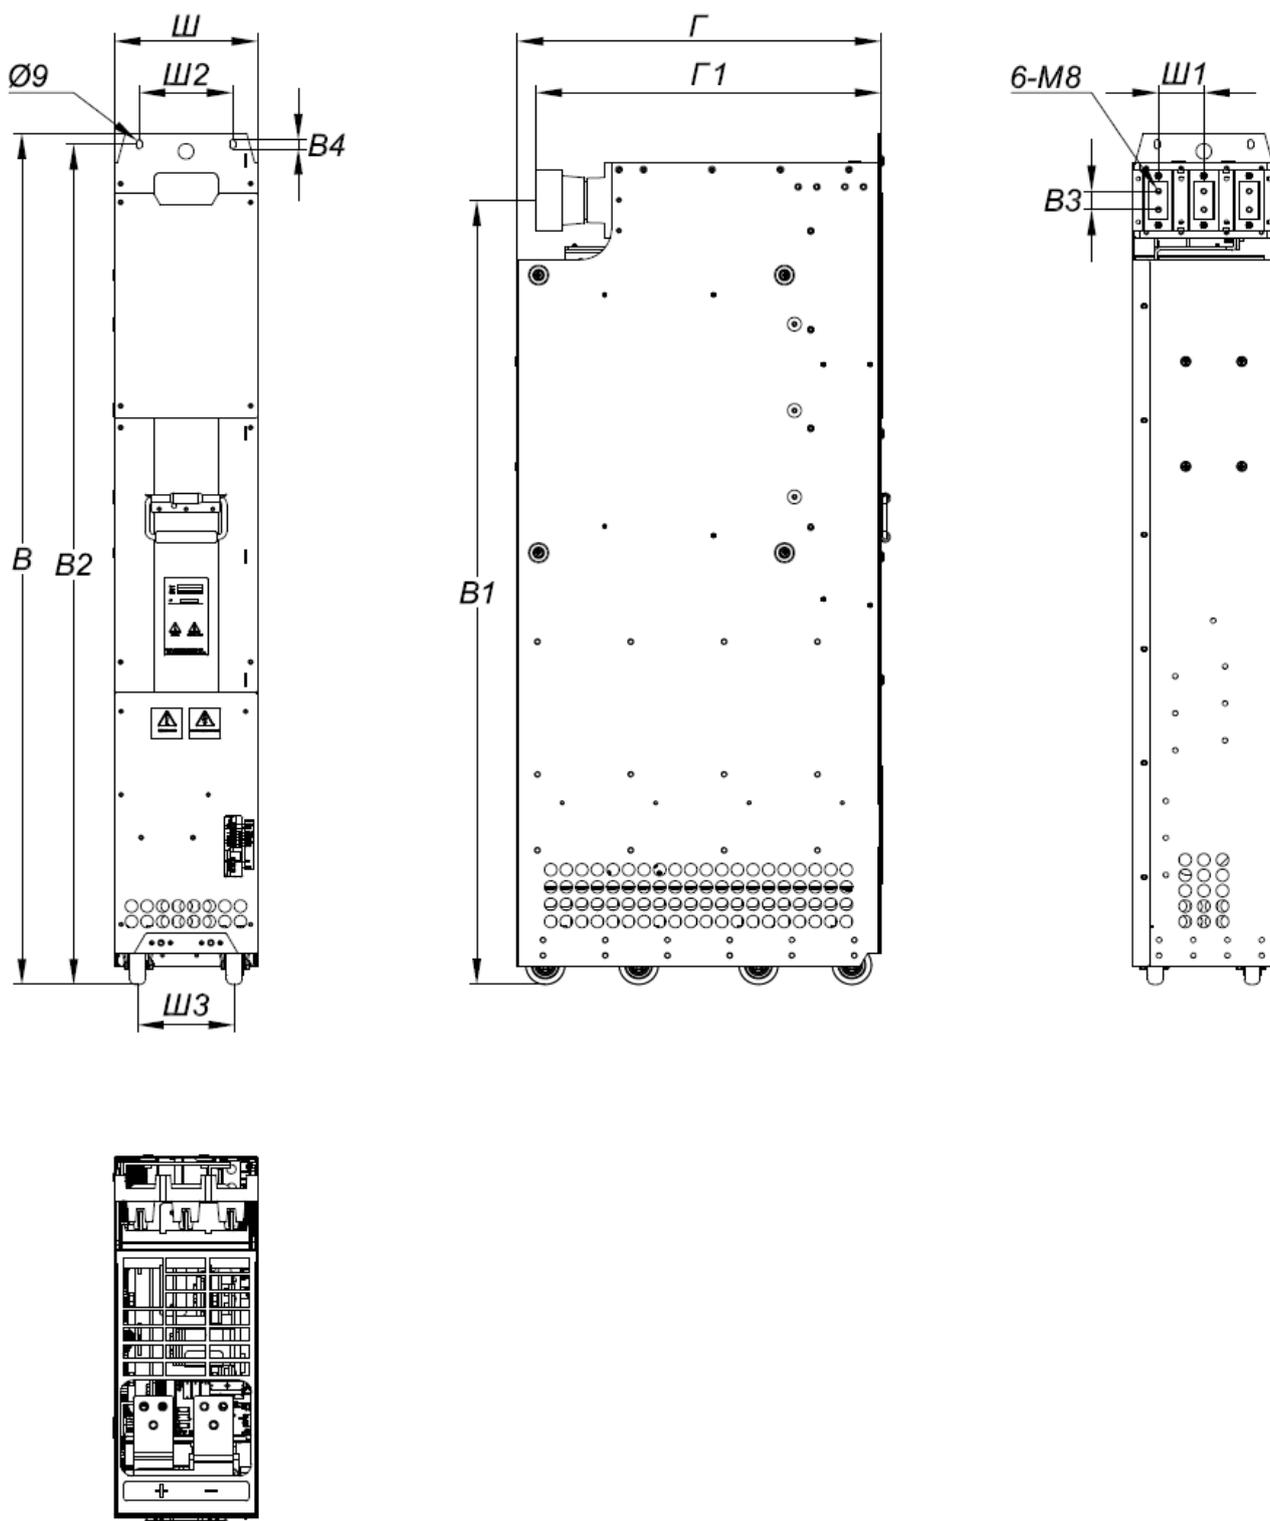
Габаритный чертеж модуля неуправляемого выпрямителя FR8T
